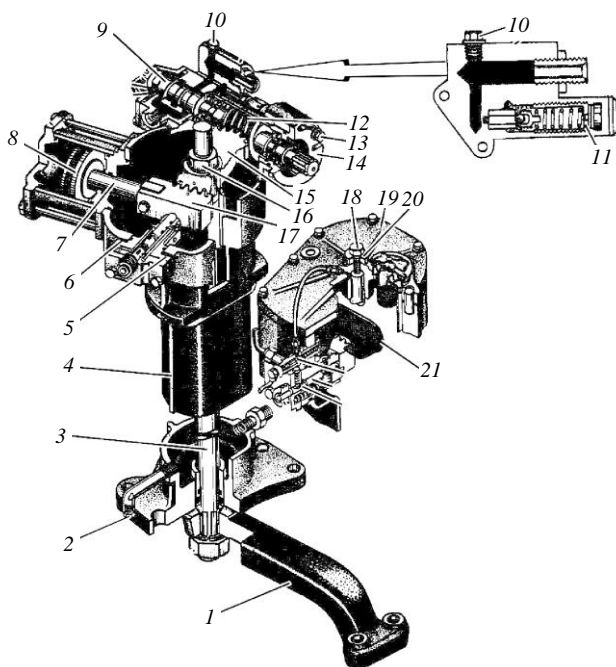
Гидроусилитель рулевого управления: 1 – сошка; 2 – сливная пробка; 3 – поворотный вал; 4 – корпус; 5 – упор рейки; 6 – регулировочные прокладки; 7 – шток; 8 – поршень; 9 – золотник; 10 – пробка; 11 – регулировочный винт клапана; 12 – червяк; 13 – болт крепления регулировочной втулки; 14 – регулировочная втулка; 15 – сектор; 16 – гайка; 17 – рейка; 18 – регулировочный болт; 19 – верхняя крышка; 20 – контргайка; 21 – сливной фильтр
